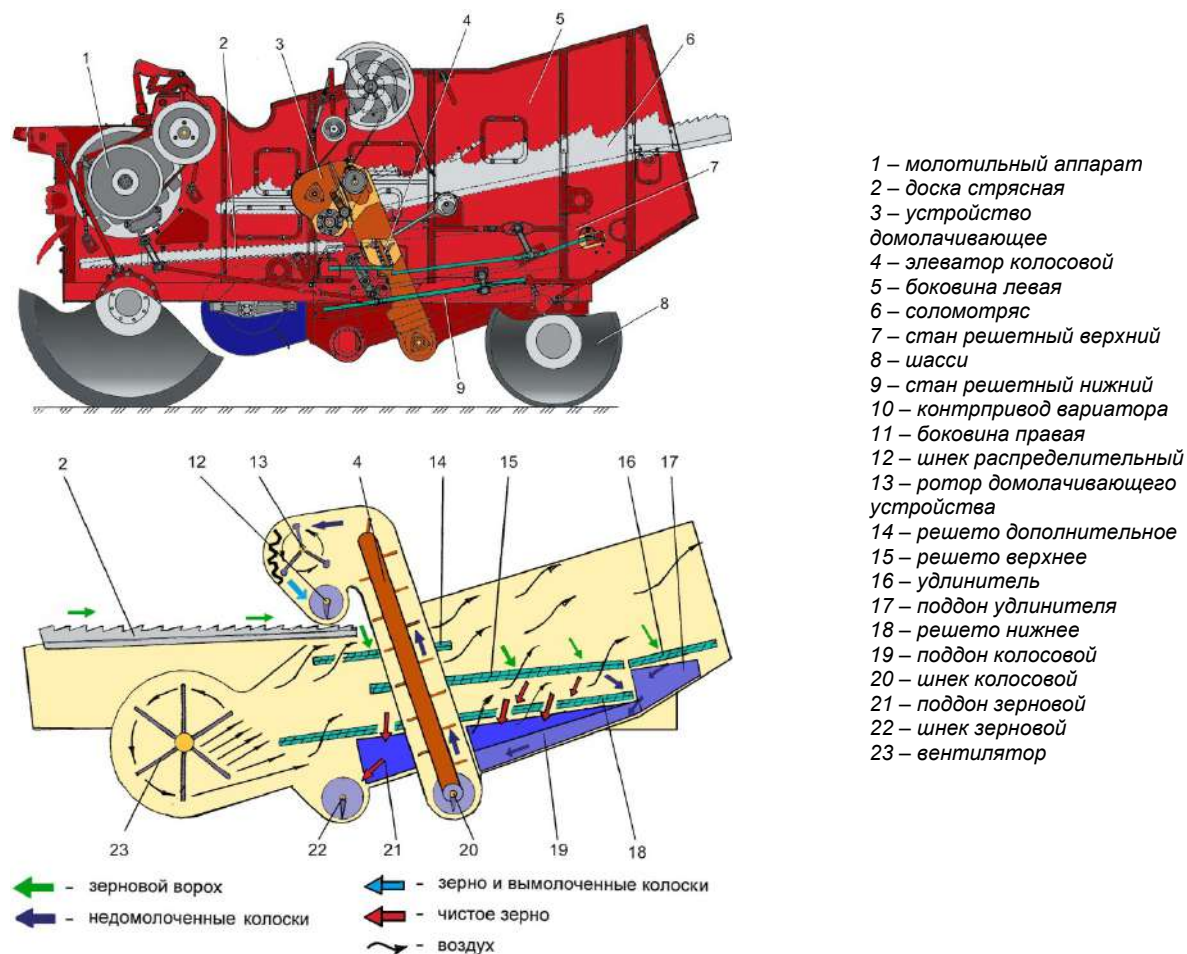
Схема работы очистки зерноуборочного комбайна.
